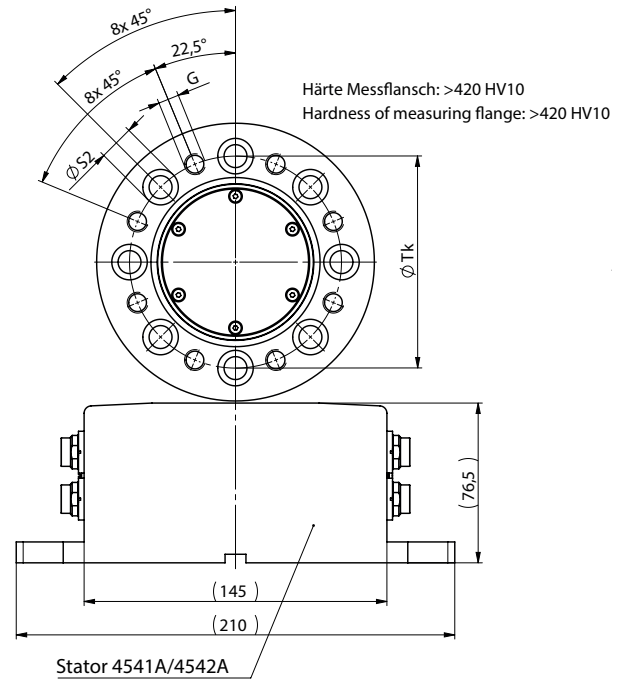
Maßzeichnung Ansicht B, KiTorq System
